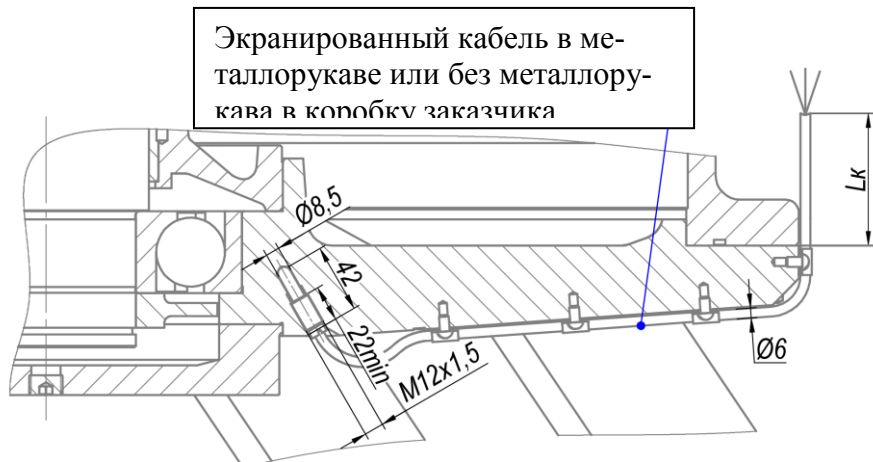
Вариант установки датчиков контроля температуры подшипников без коробки выводов двигателей ВАБ450
